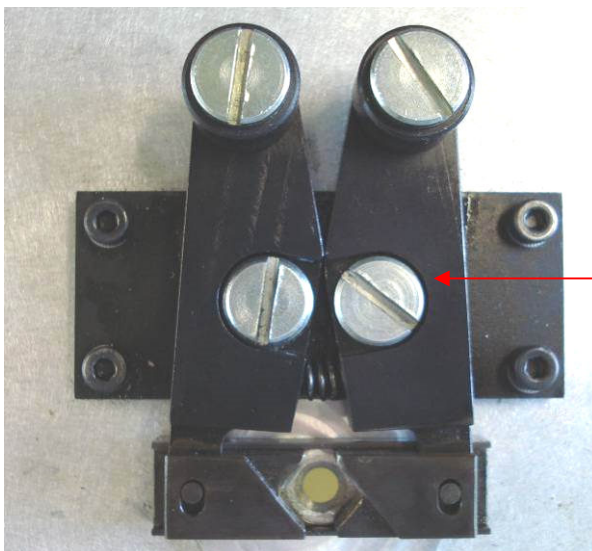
Hülseaufnahme / Ferrule adapter
